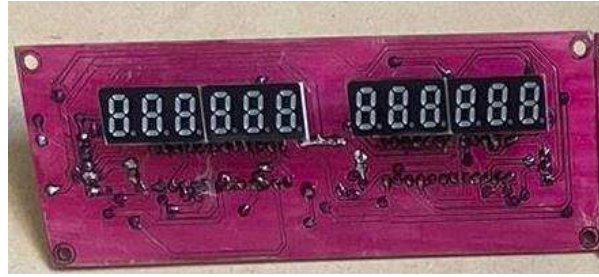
Impresión parte delantera circuital display 7 segmentos COM y NAV finalizada
